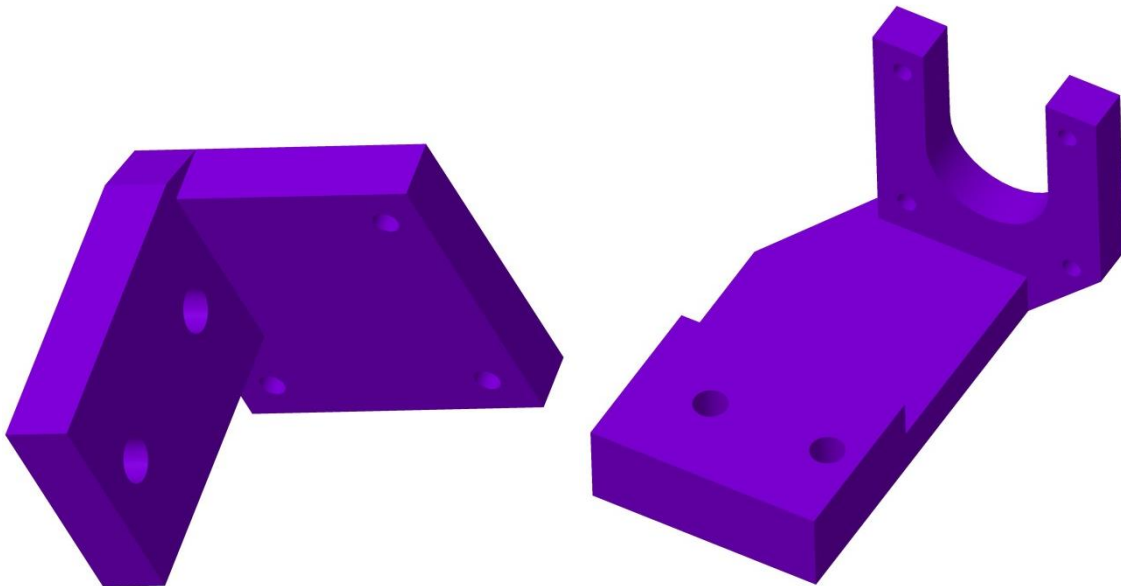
Sestava rámu dávkovače s hlavními komponentami
